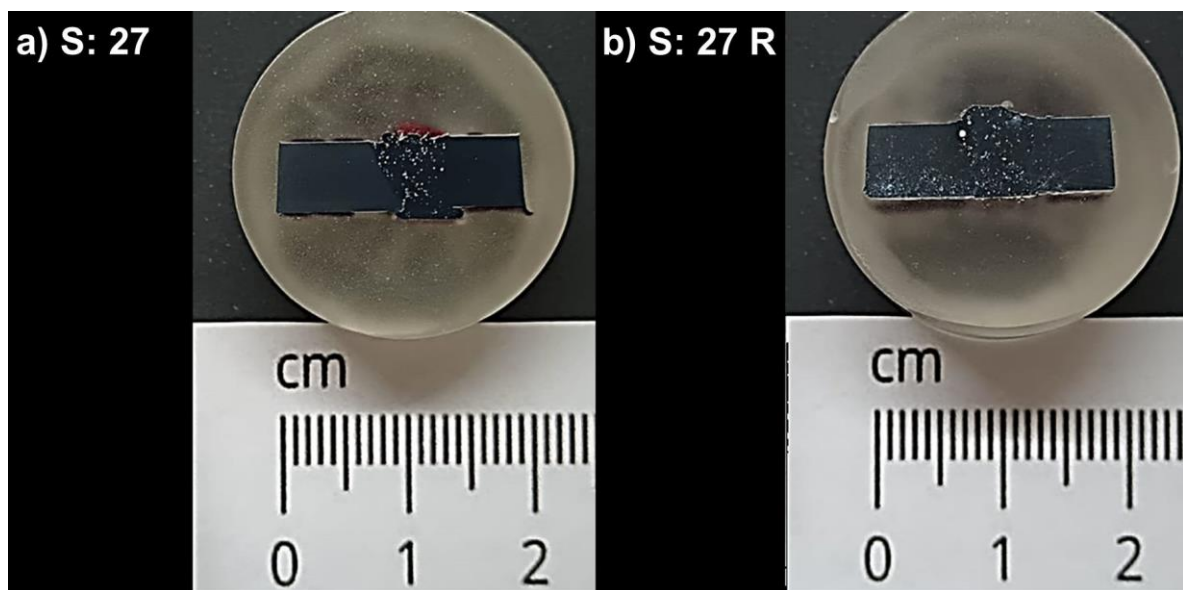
68 Soldadura 27 y soldadura 27 R montadas en resina acrílica con acabado espejo.
